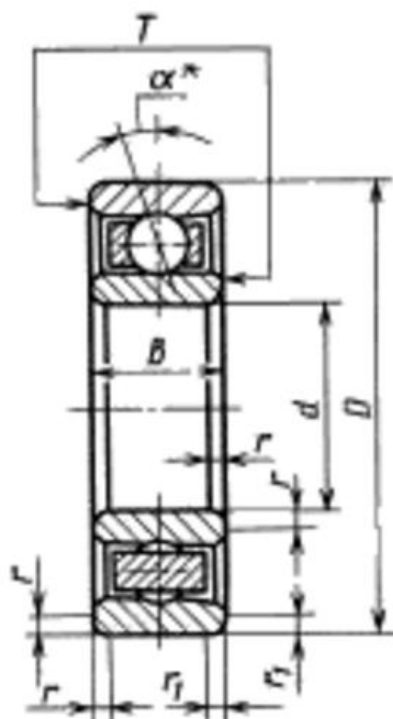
Радиально-упорный шариковый однорядный подшипник.
